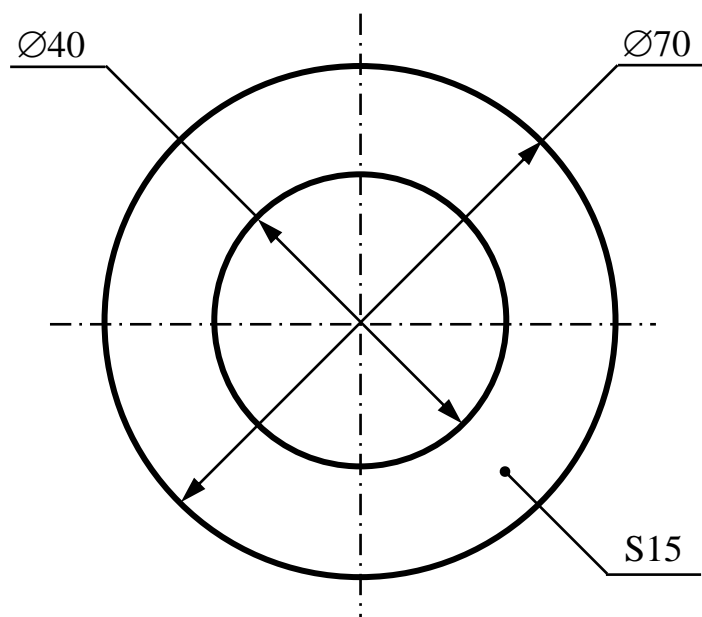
Ескіз заготовки для виготовлення зразків.
